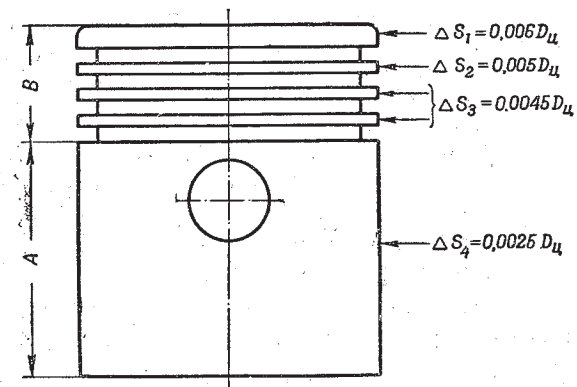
Зазоры между поршнем и цилиндром для алюминиевых сплавов
